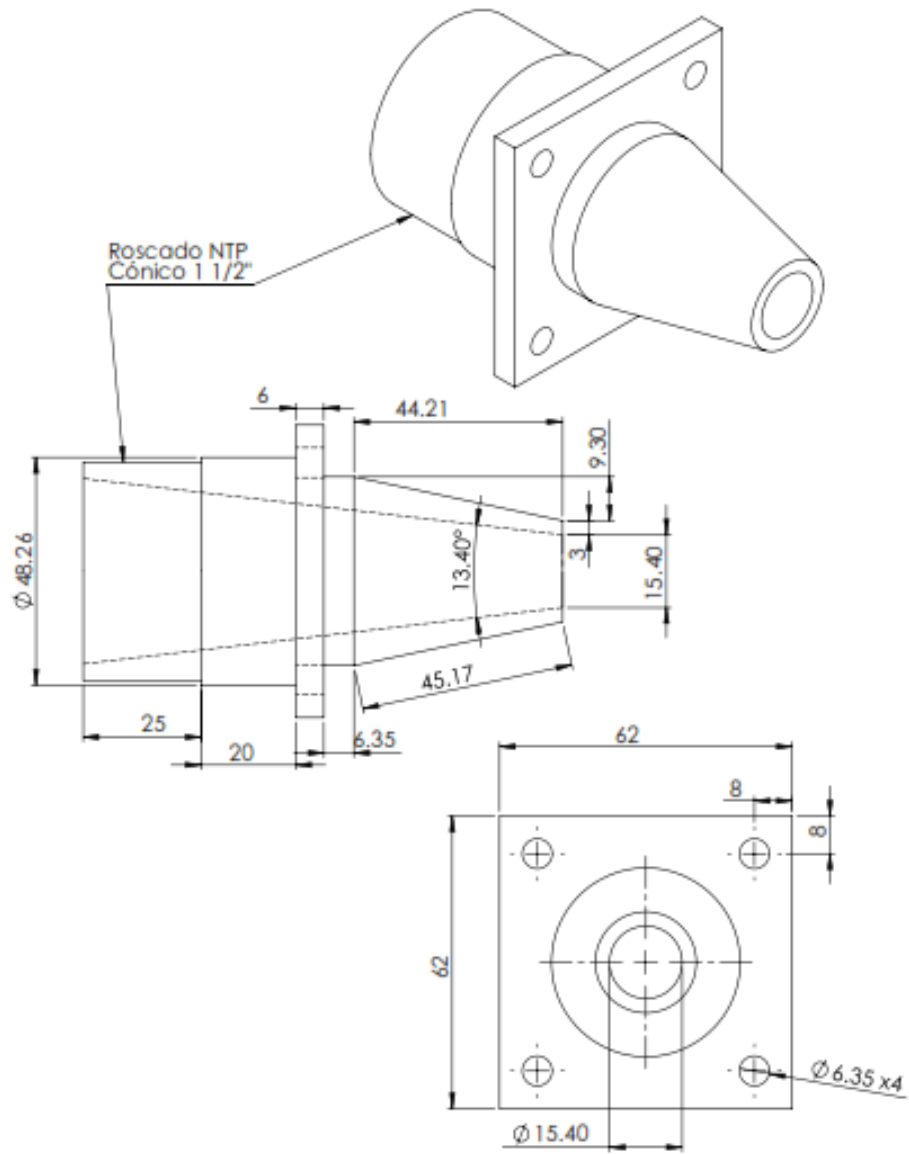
Plano de taller del inyector (cotas en mm). Fuente: Autores.
